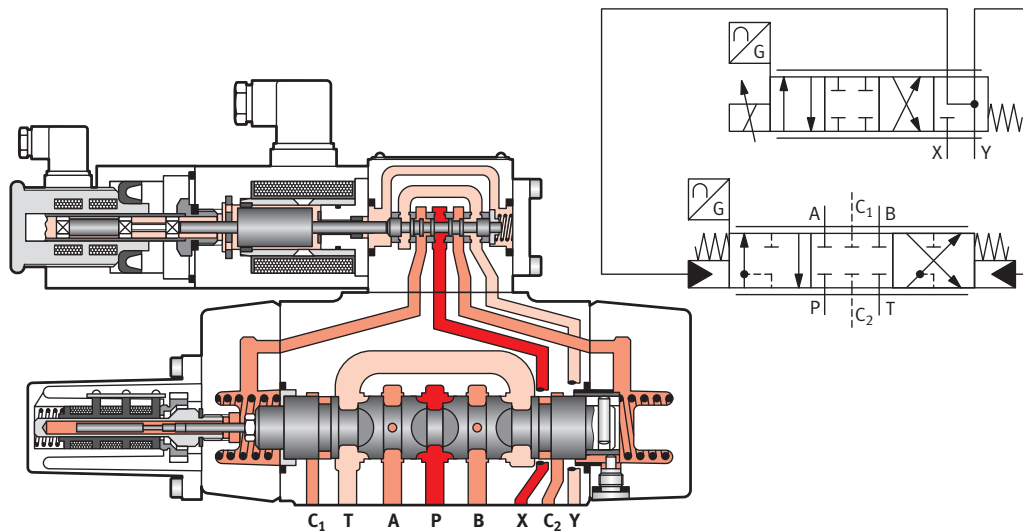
Válvula posicionadora servopilotada, con regulación de posiciones. Vista en corte y símbolo.
